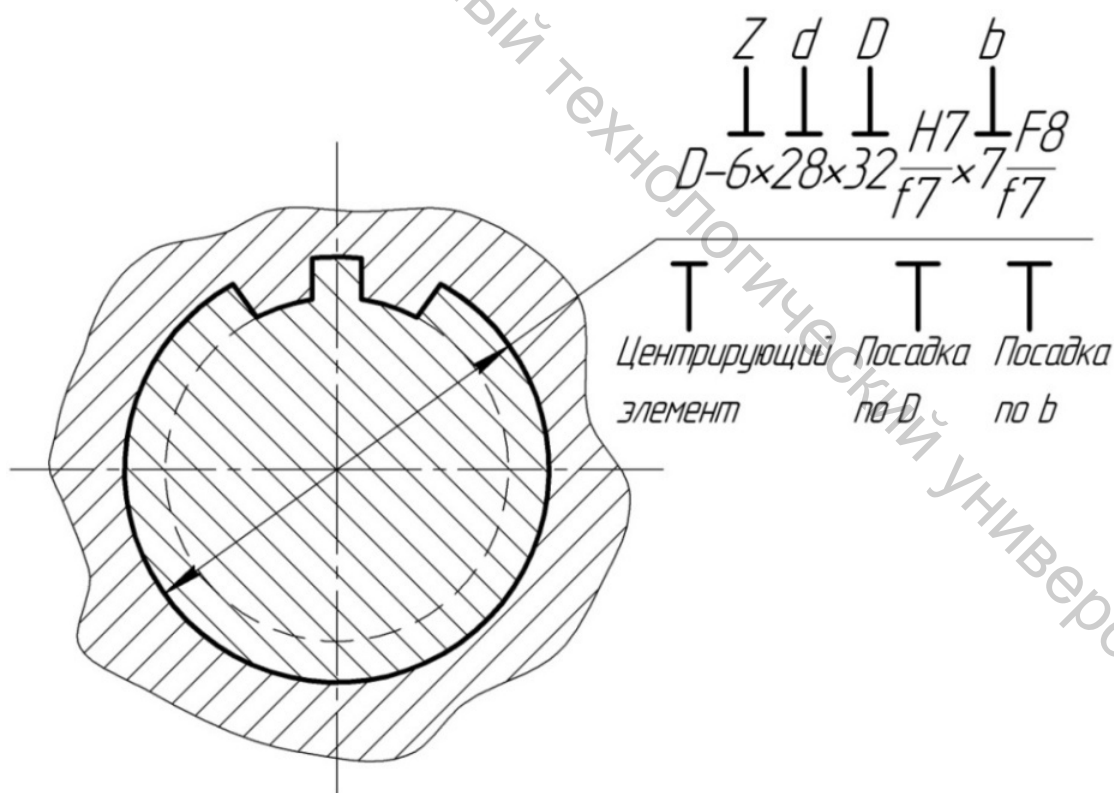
Обозначение шлицевого соединения на сборочном чертеже
